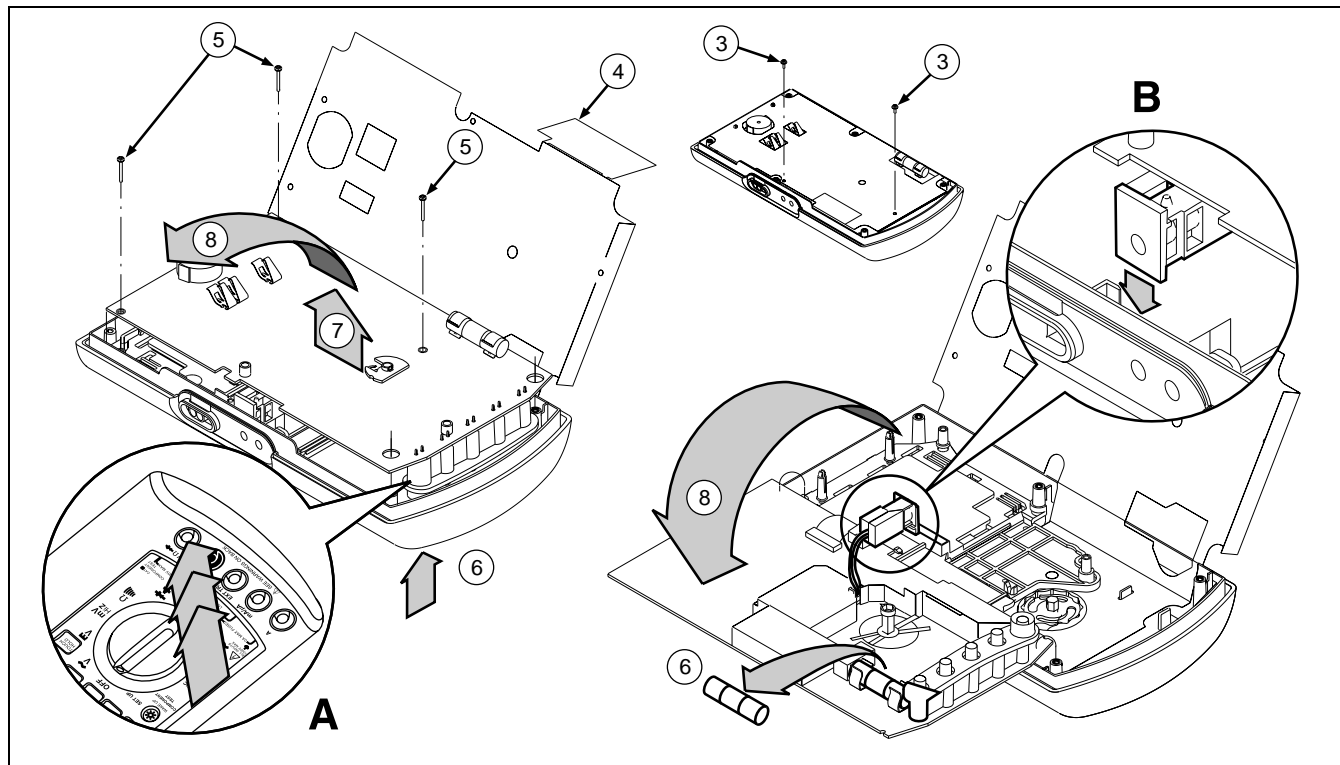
Remplacement du fusible 11A (haute énergie)
